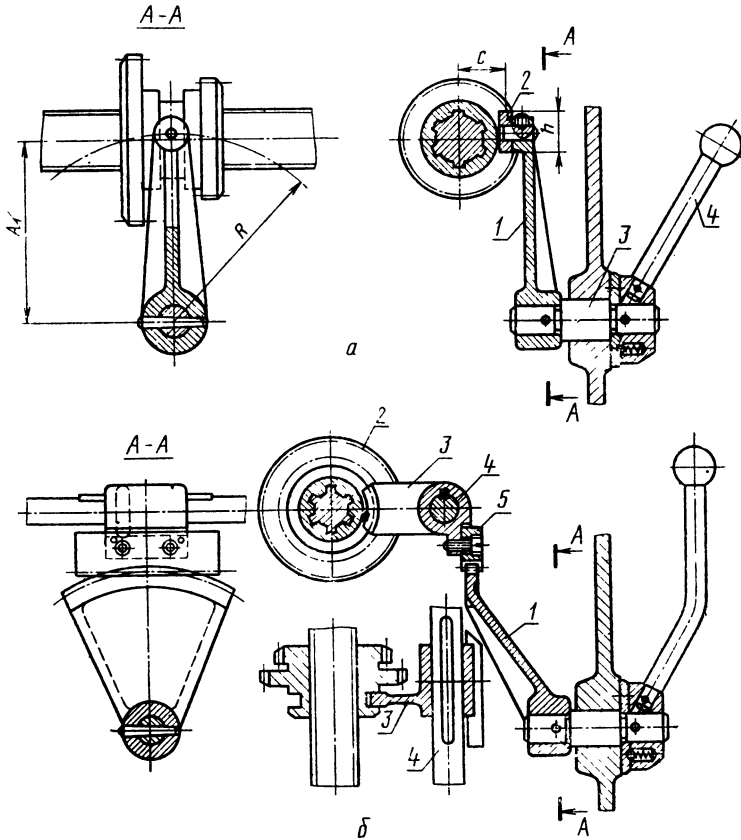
Схемы механизмов перемещения зубчатых колес по валам
